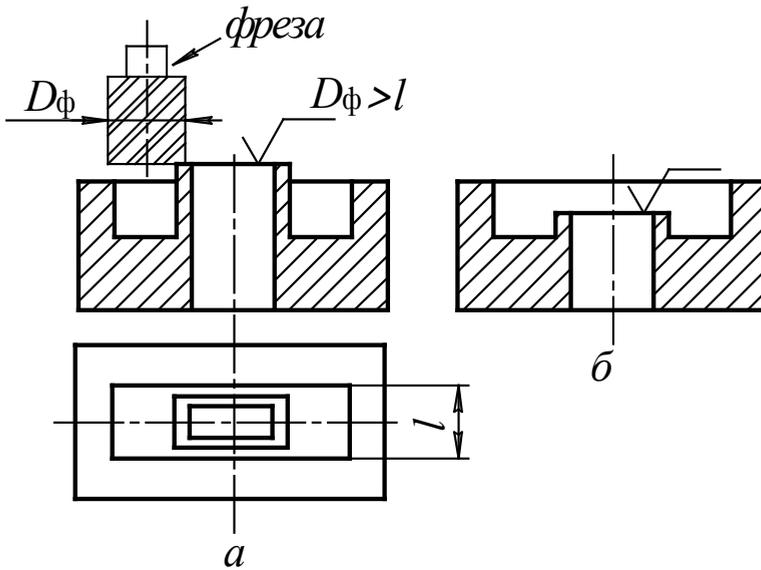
Конструкция корпусных деталей с пазом и бобышкой:
